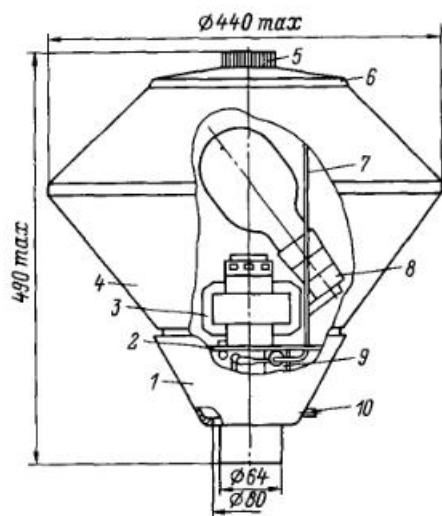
Конструкция светильников типа РТУ01-250/С53-01-У1
